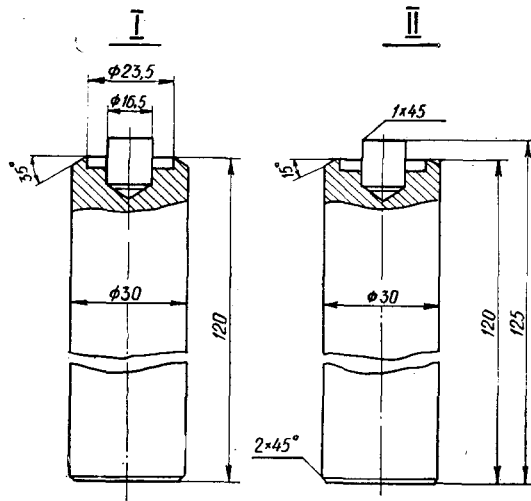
Приспособление для развальцовки обоймы подшипника ШС-12:
